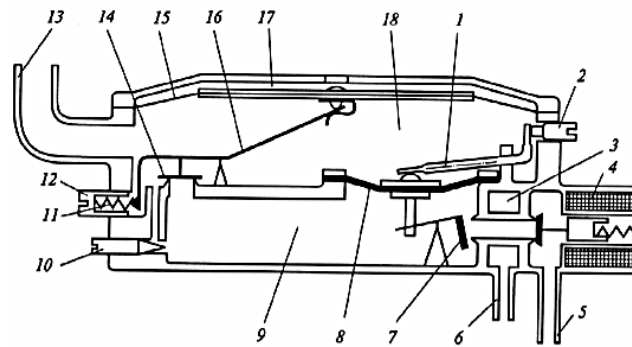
Схема редуктора-испарителя низкого давления ЗАО «Автосистема»: 1 - торсионная пружина; 2 - винт регулировки давления 1-й ступени; 3 - полость для теплоносителя; 4 - катушка электромагнитного клапана; 5 - вход газа; 6 - входной штуцер для подвода охлаждающей жидкости; 7- клапан 1-й ступени; 8 - мембрана 1-й ступени; 9 - камера 1-й ступени; 10 - винт регулировки холостого хода; 11 - пружина; 12 - регулировочный винт 2-й ступени; 13 - выходной патрубок; 14 - клапан 2-й ступени; 15 - мембрана 2-й ступени; 16 - рычаг клапана 2-й ступени; 17 - камера атмосферного давления; 18 - камера 2-й ступени
